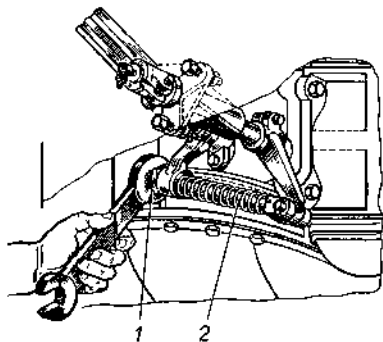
Регулировка свободного хода педали сцепления при механическом приводе: 1 — гайка; 2 — тяга
